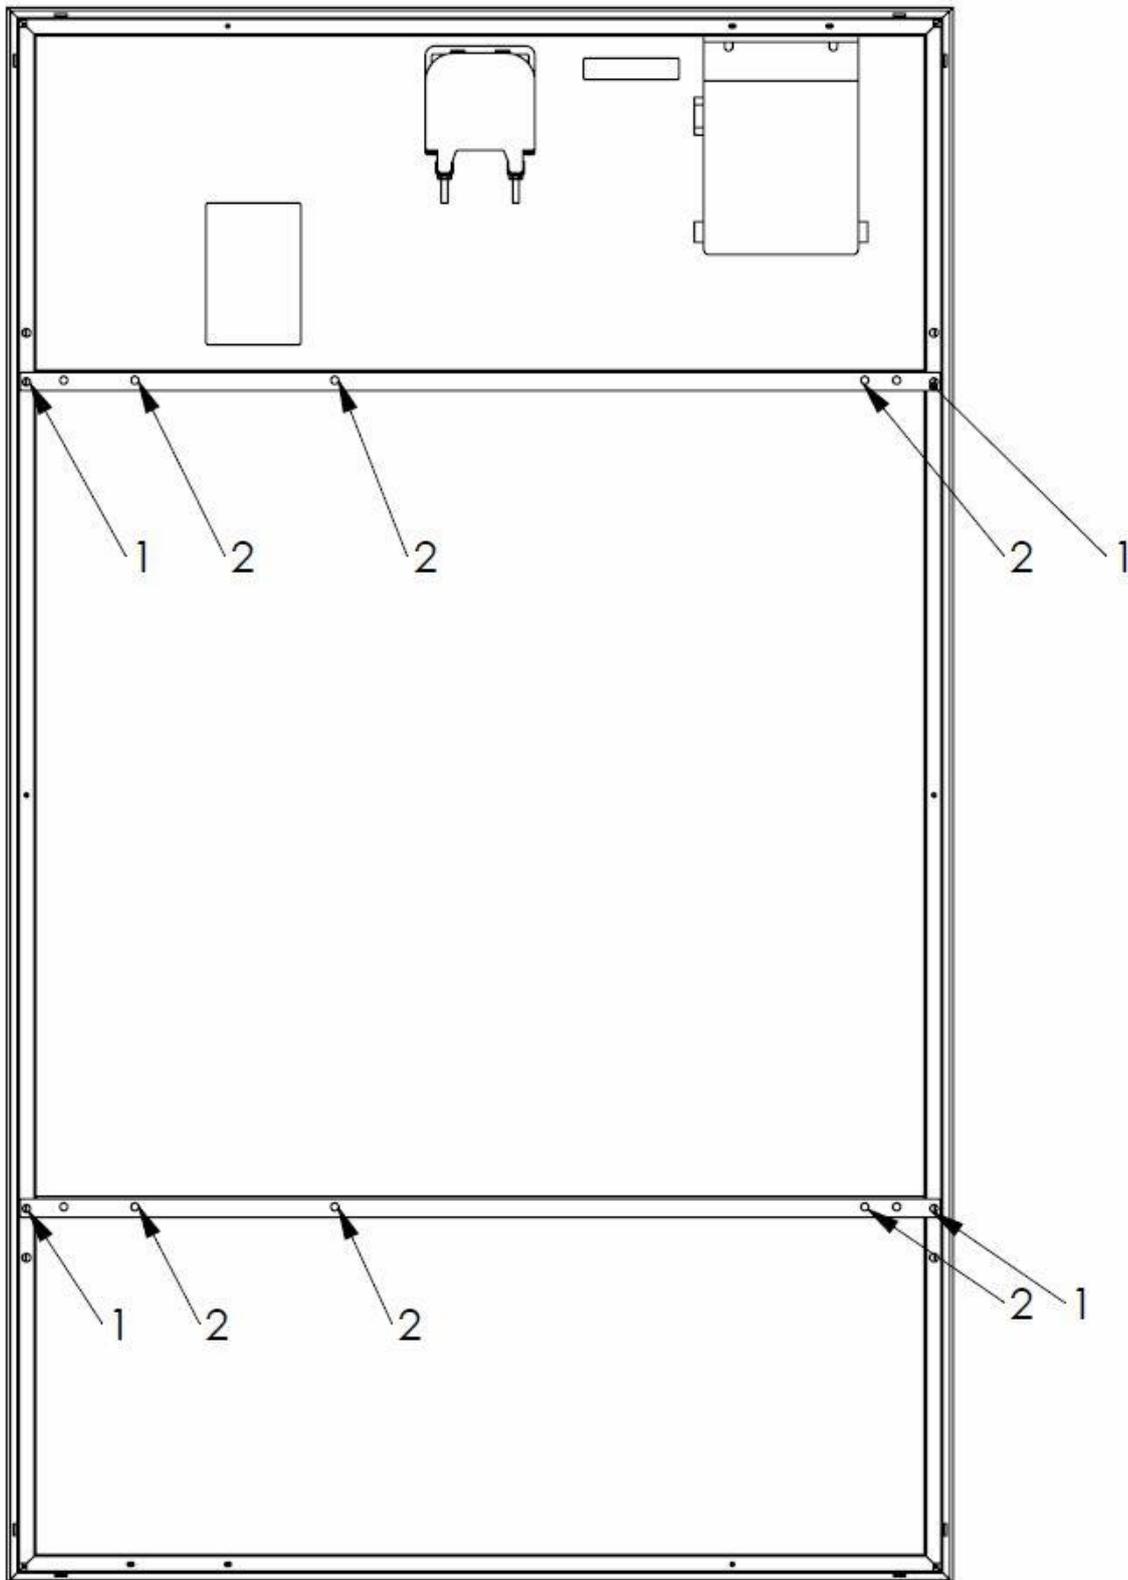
Schraubenpositionen für die Montage auf Standfüßen
